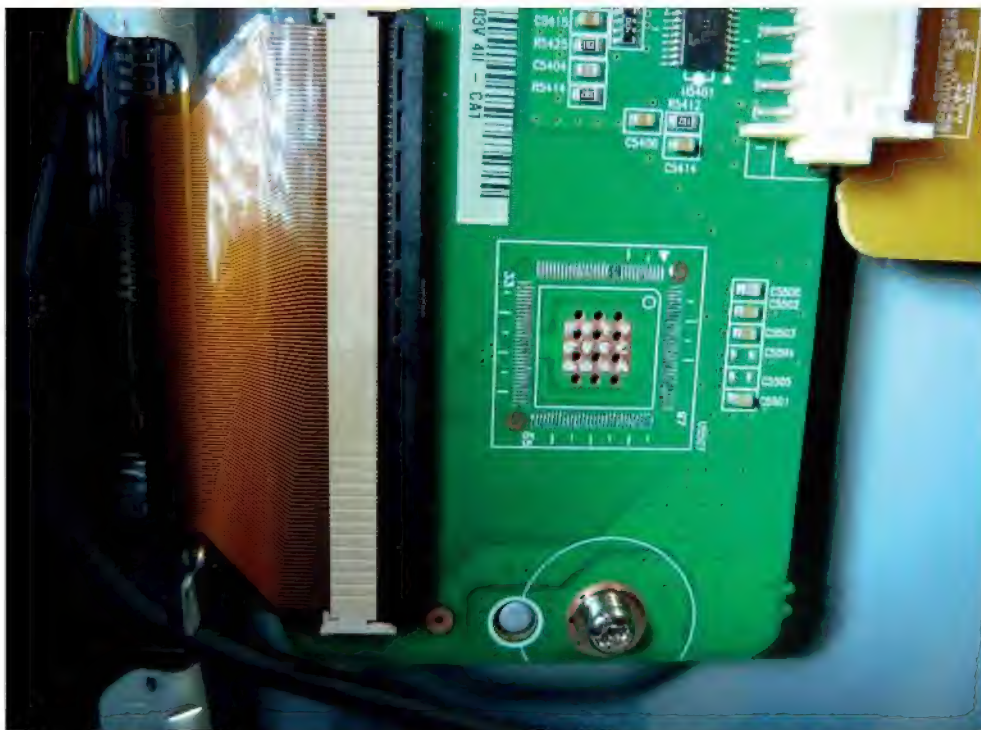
Carte Y-buffers après dessoudage du circuit R2A20292BFT
